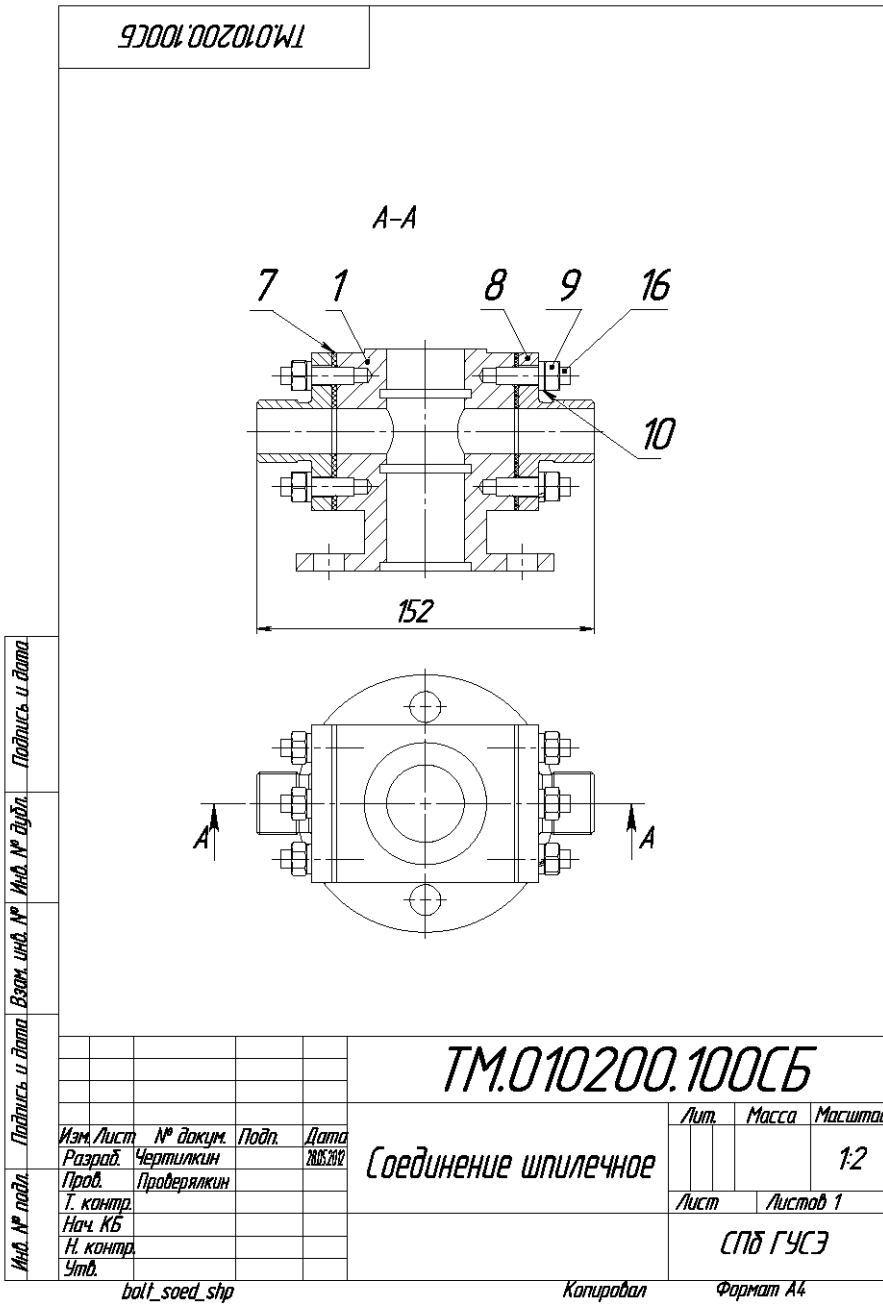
Сборочный чертеж соединения шпильчатого
